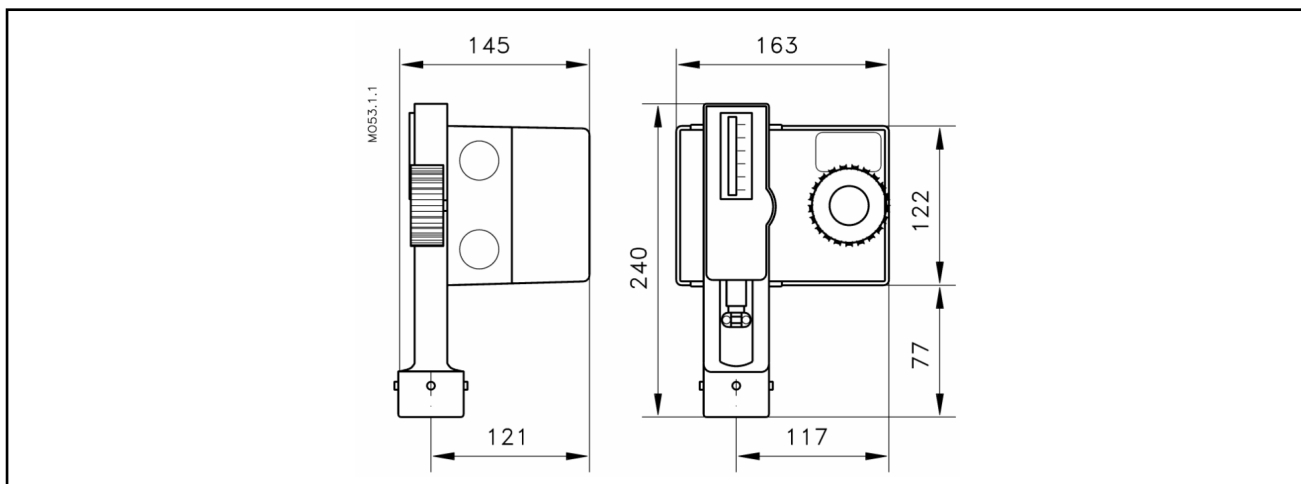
Габаритные и присоединительные размеры AMV 323, 423, 523.
